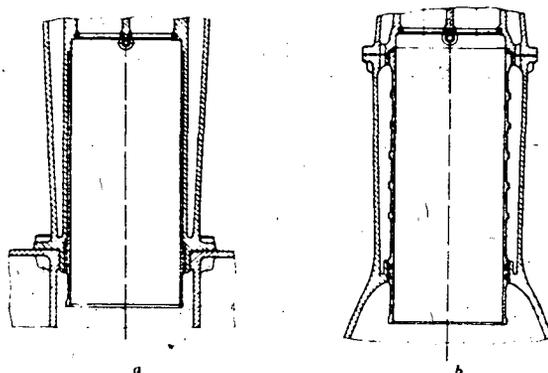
Beispiel einer trockenen (a) und einer nassen (b) Zylinderlaufbüchse
